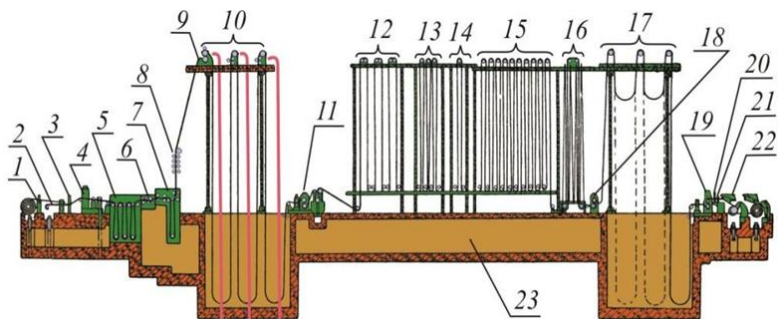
Схема непрерывной линии отжига полосы: 1 – разматыватель; 2 – натяжные ролики; 3, 21 – ножницы; 4 – сварочная машина; 5 – ванна для электролитической очистки полосы; 6 – ролики для перегиба полосы при механической очистке ее поверхности; 7 – горячая промывка; 8 – приводные ролики; 9, 11, 18, 19 – натяжные ролики; 10 – шлеппер №1 (аккумулятор полосы); 12–16 – зоны нагрева, выдержки, медленного, быстрого и окончательного охлаждения; 17 – шлеппер № 2; 20 – вырезка образцов; 22 – моталка; 23 – помещение для электроаппаратуры
